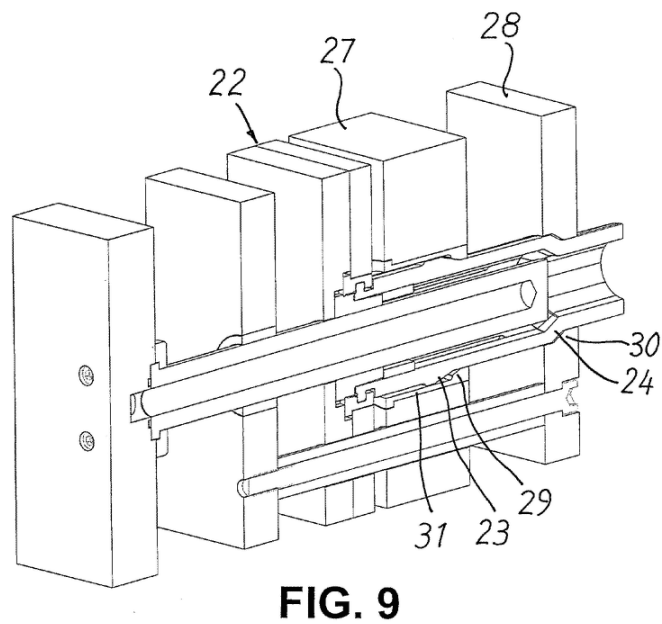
Patent, Expandable core pin for blow-molding a container having...
